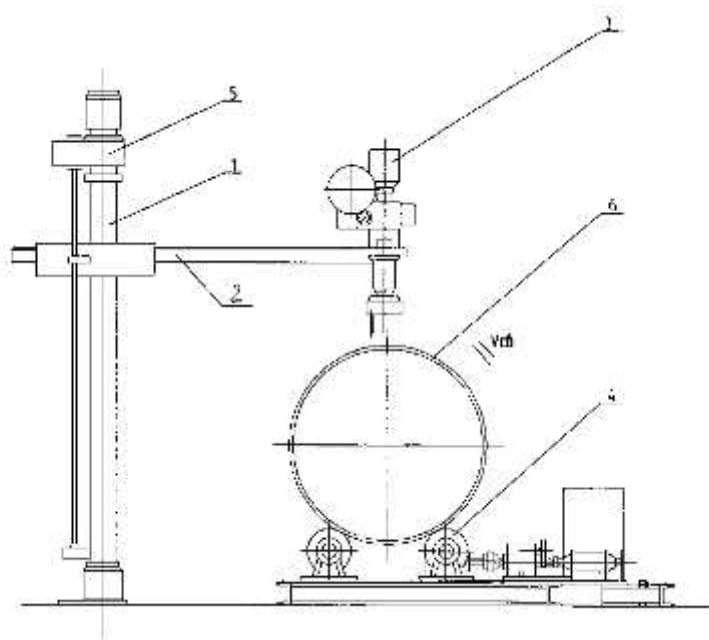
Установка 2/RMB2.0x2.0 для автоматической сварки
